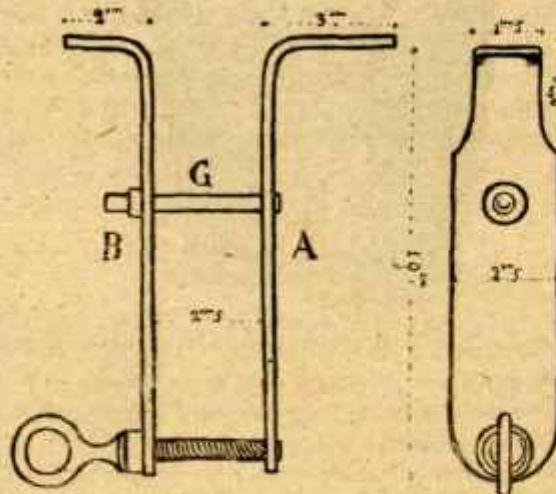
El separador visto de perfil y de frente. Sus dimensiones.
